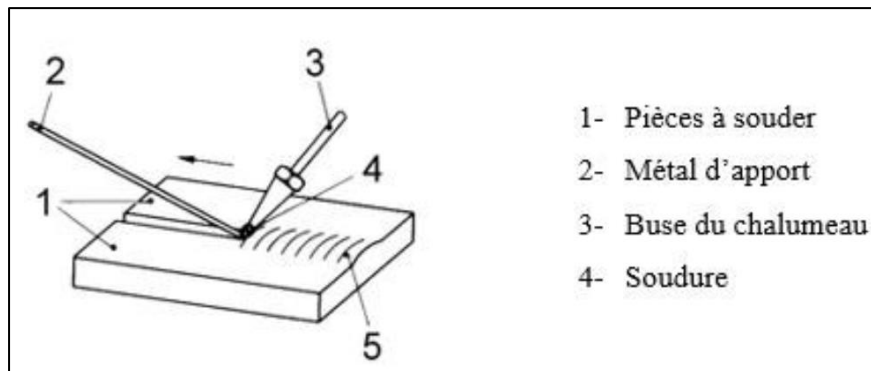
Exécution d'une soudure au chalumeau
